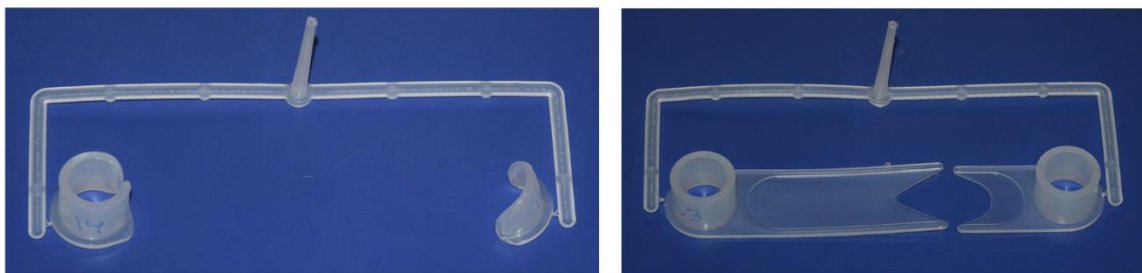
1 Piezas fabricadas que presentan un llenado incompleto de la cavidad del molde
